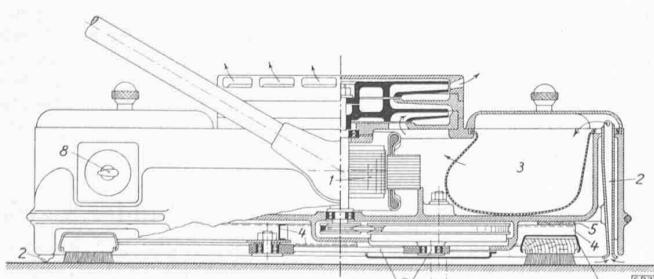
Bodenspän-Maschine GEBR. BÜHLER, Uzwil. — Schnitt 1:9
